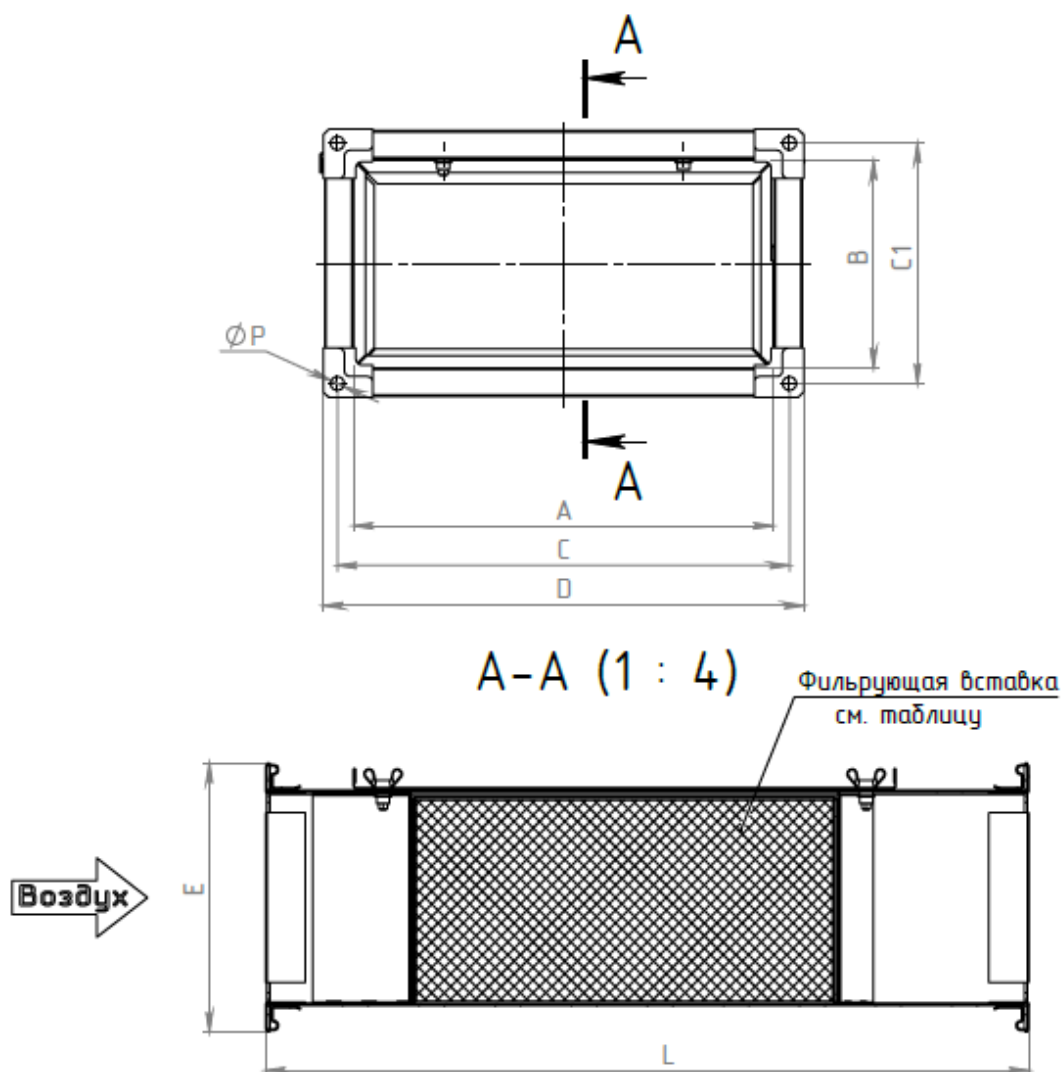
Внешний вид и основные размеры фильтров КРН
